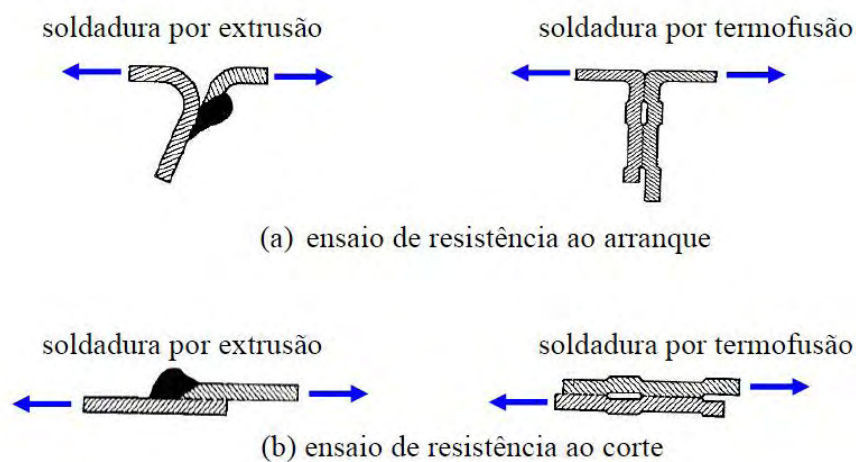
Ensaio de resistência ao arranque e ao corte de soldaduras.
